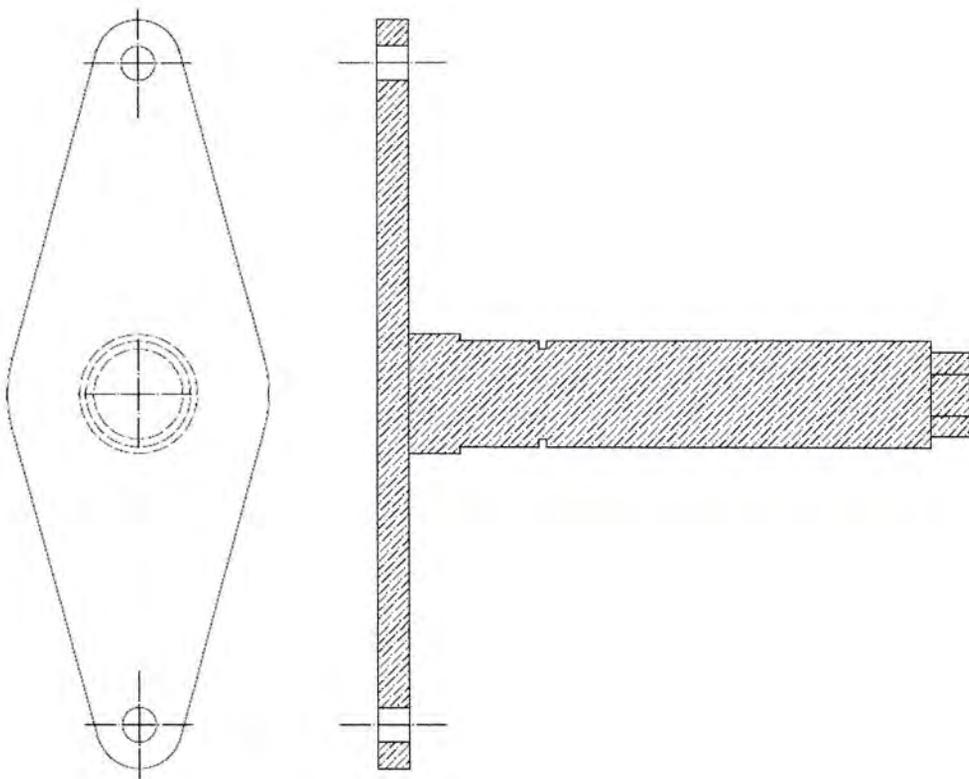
Plat join pipa engkol, 1 pc
